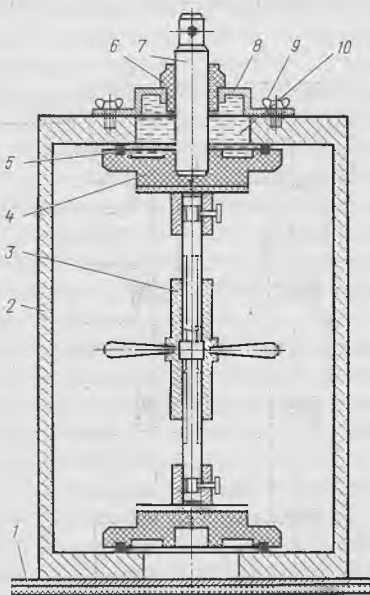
Приспособление для вневанного железнения отверстия под подшипник в картере коробки передач:
